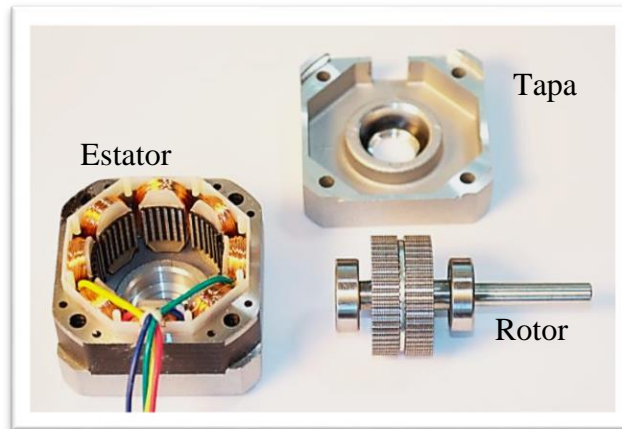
DESPIECE MOTOR PASO A PASO
